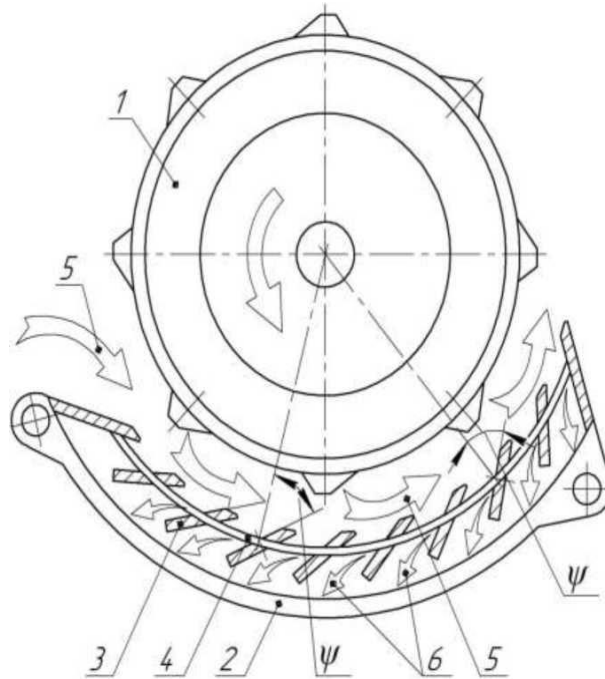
Молотильний пристрій: 1 – барабан; 2 – підбарання; 3 – поперечні планки; 4 – поздовжні прутки; 5 – хлібна маса; 6 – вільне зерно.
